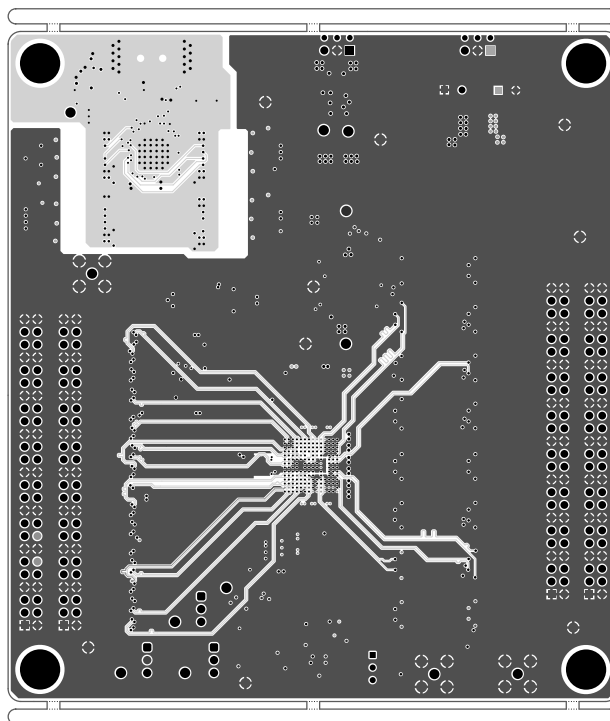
PCB 第 7 层 (接地 4/信号 4)
